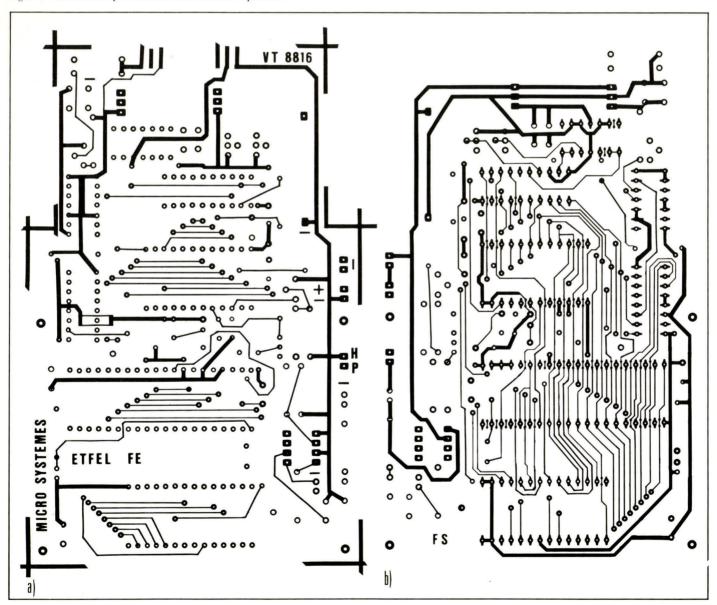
a) Circuit imprimé vu côté composants; b) vu côté soudures.
